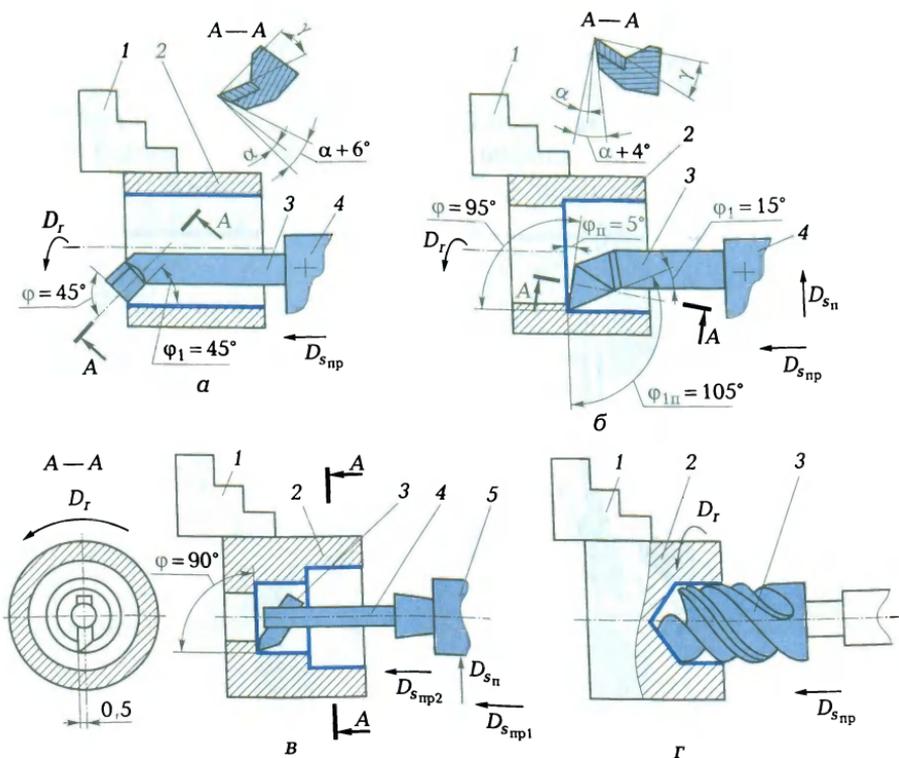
Схемы обработки отверстий заготовок, закрепленных в патроне, на токарно-винторезном станке:
